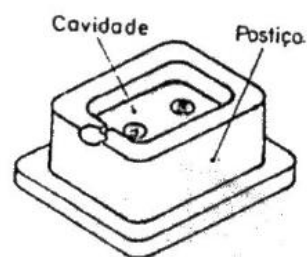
Placa Suporte com postigo (adaptado de [9])
